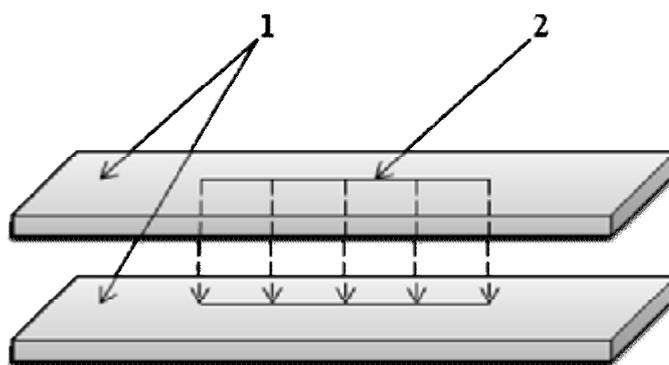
Структура исследуемых пластин Метгласа: 1) пластины Метгласа; 2) сварочный шов
